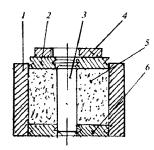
Пресс-форма (до прессования): I — кольцо; 2 — верхняя формовочная плита; 3 — оправка; 4 — дополнительная плита; 5 — формовочная смесь; 6 — нижняя формовочная плита
